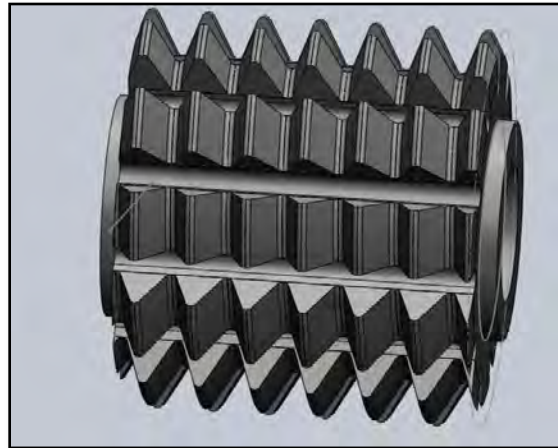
12. Diseño 3 de fresa madre de módulo 4.0425 mm.
